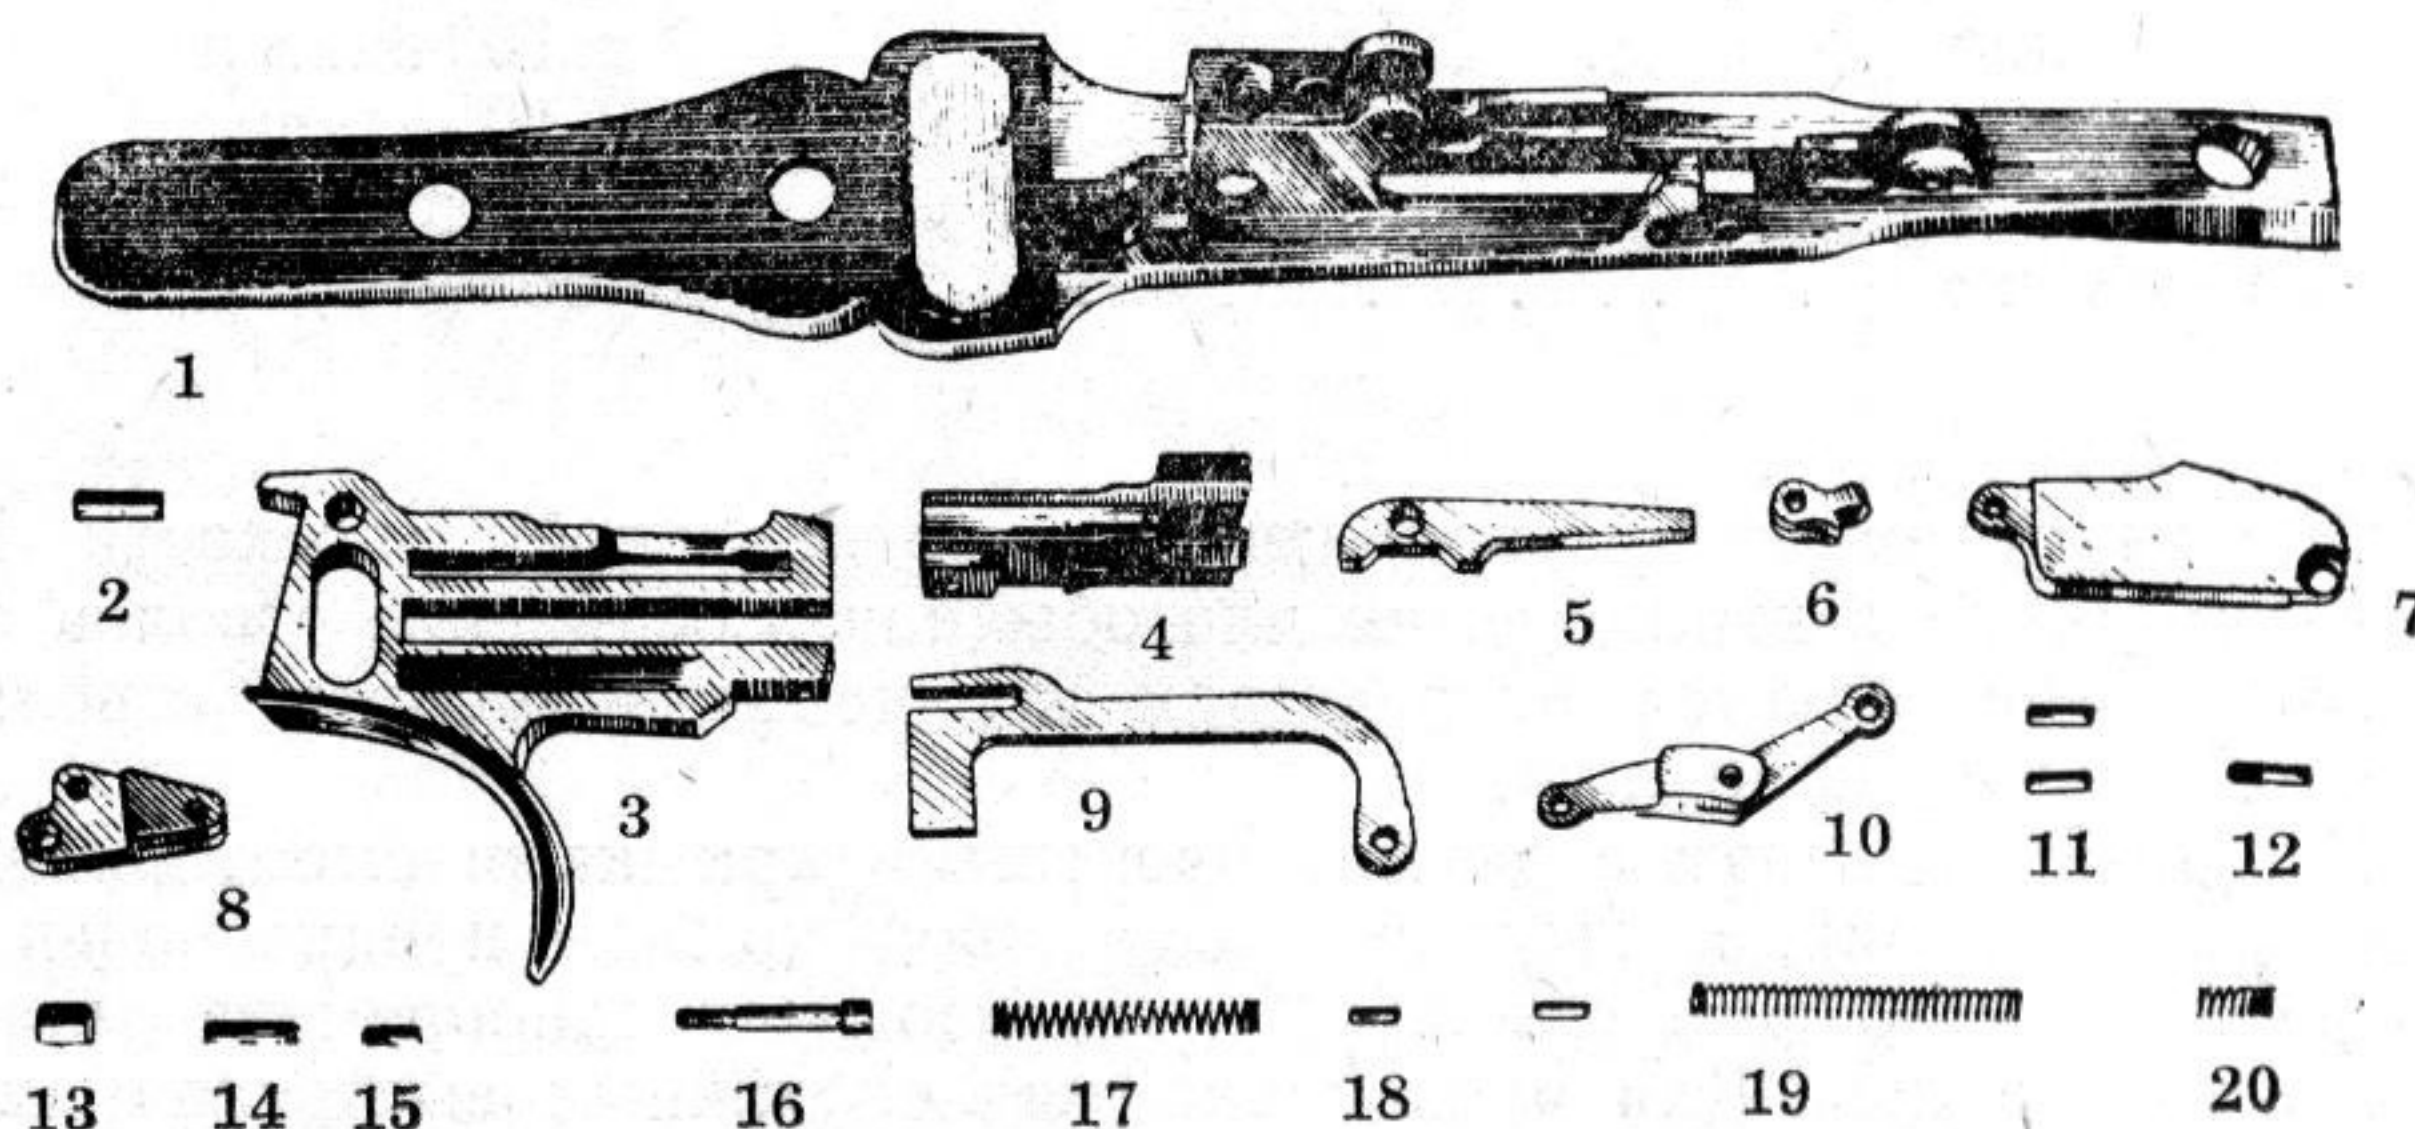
Детали спускового механизма ружья МЦ 111—01:
